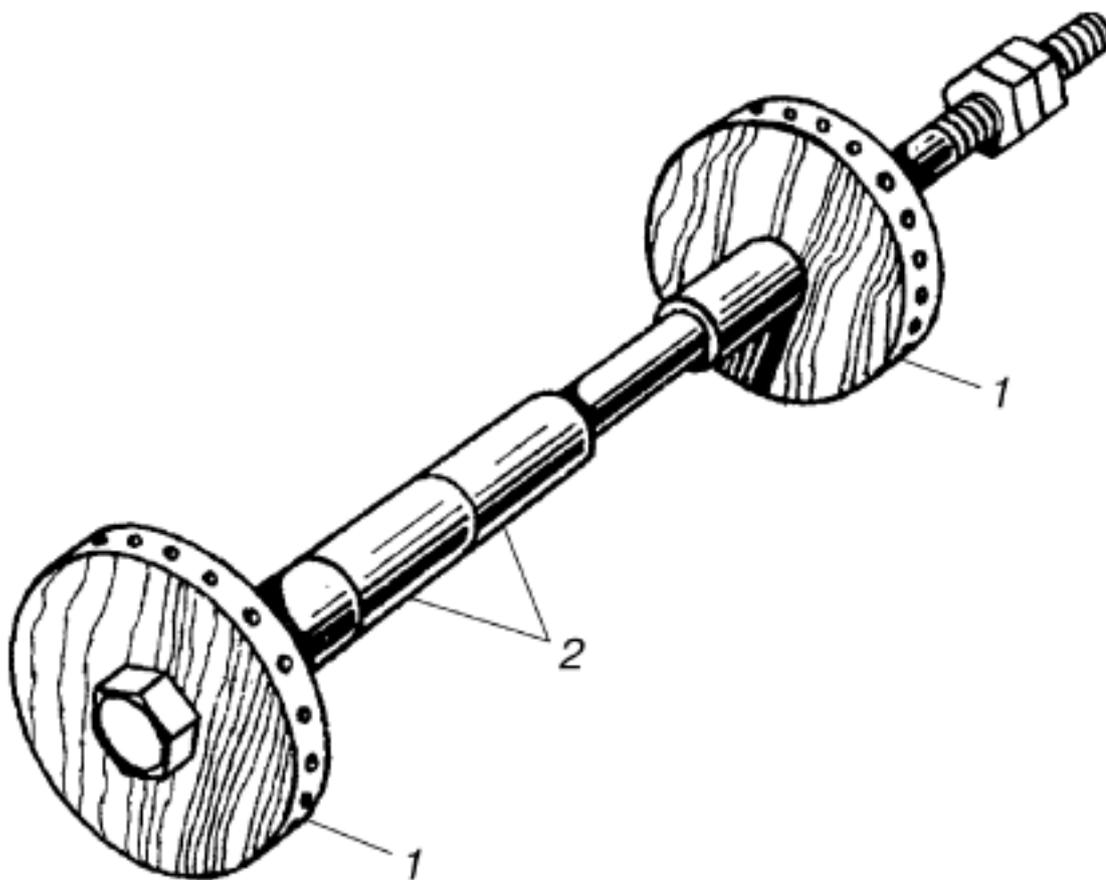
Универсальное приспособление: 1 – вставки, 2 – трубки
